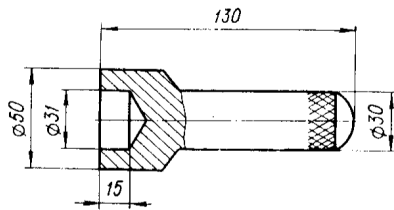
Оправка для напрессовки подшипника на зубчатый хвостовик
